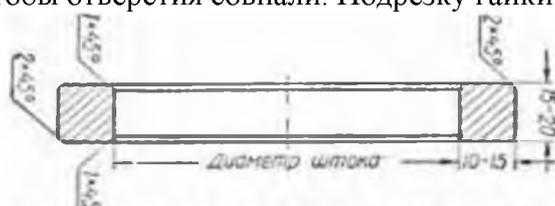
Кольцо-калибр для контроля обработки штока поршня.
